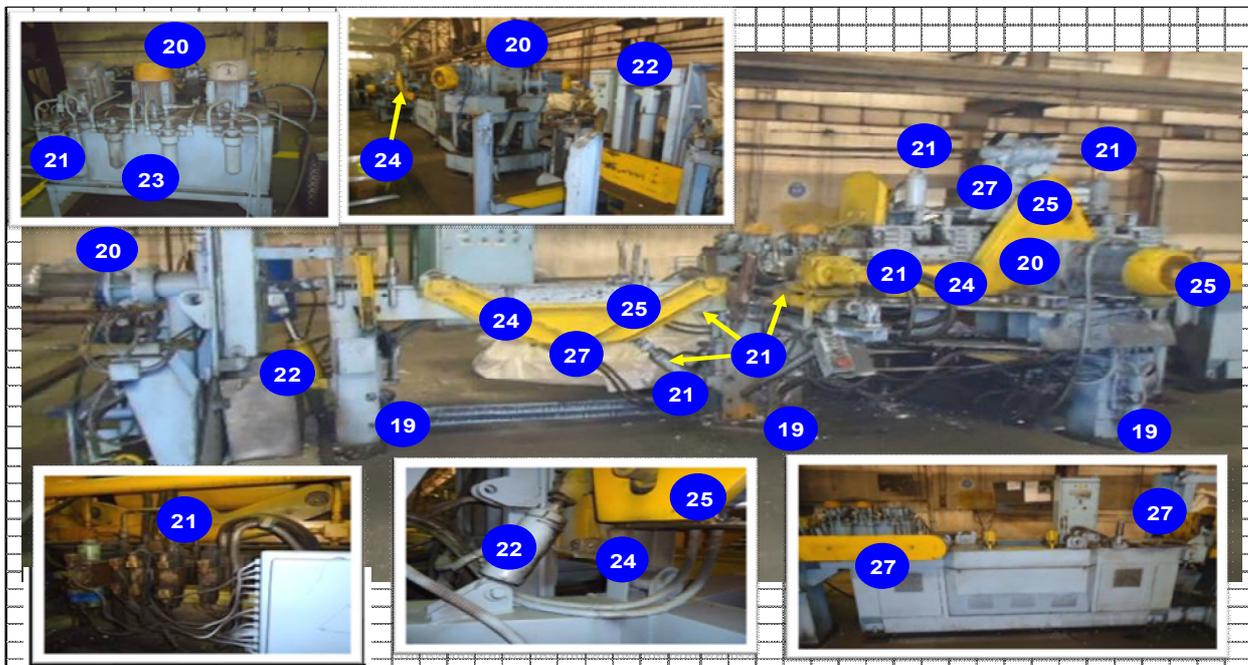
Схема установки для изготовления штанг анододержателей
